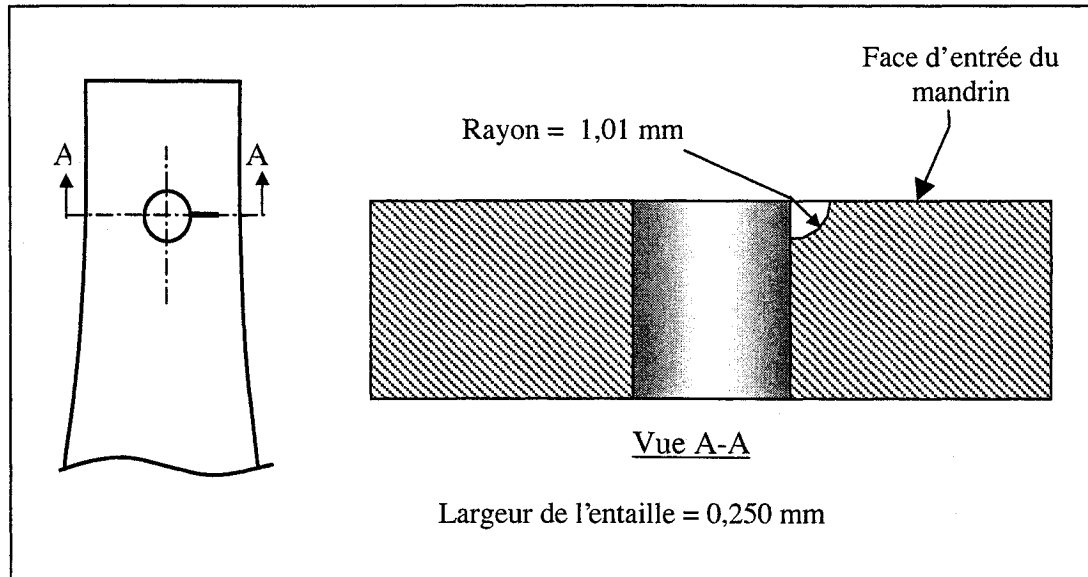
Géométrie et dimensions de l'entaille initiale
